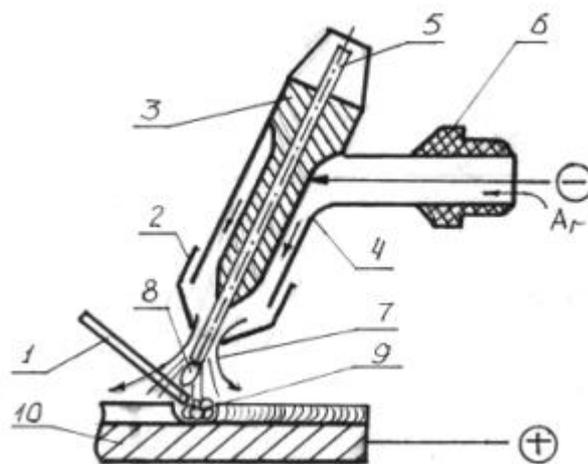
Схема электродержателя для аргонно-дуговой сварки:
